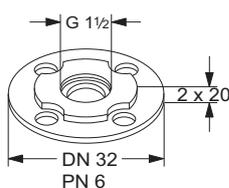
Beispiel eines Gewinde/Flansch-Adapters
